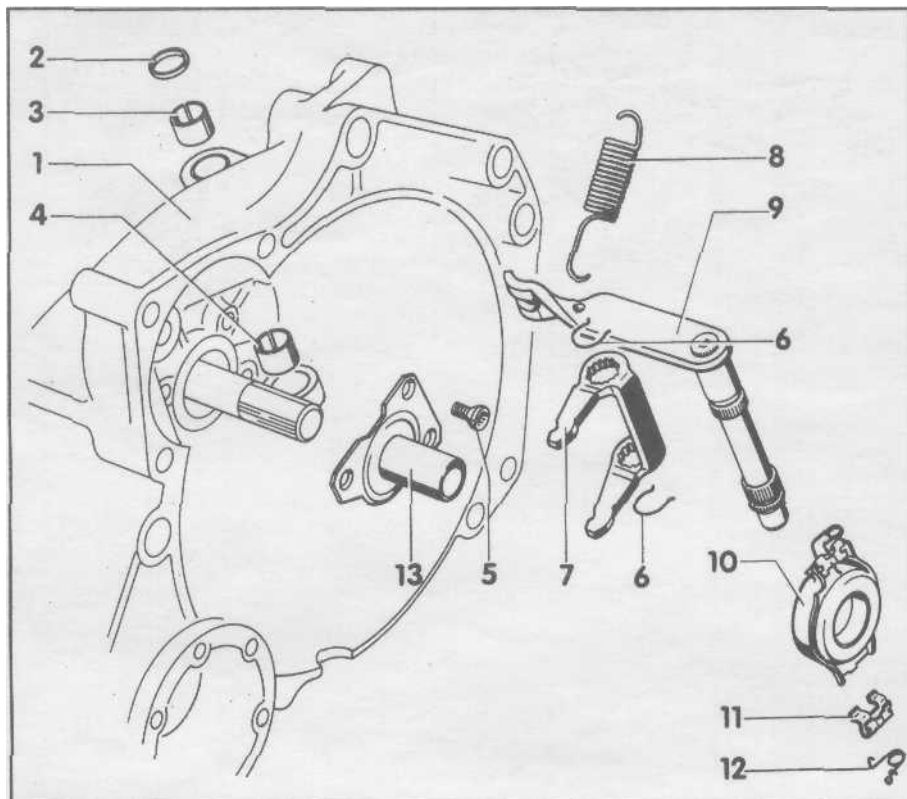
Детали механизма выключения сцепления - коробка передач 085
